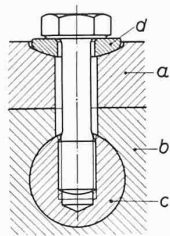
Ausführungsform für eine häufig zu lösende Stiftschraube bei Leichtmetallteilen.
